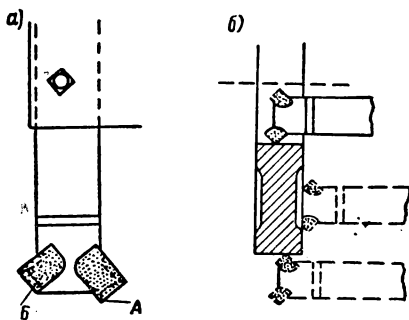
Обработка заготовки для цилиндрической шестерни с помощью специального комбинированного резца.
